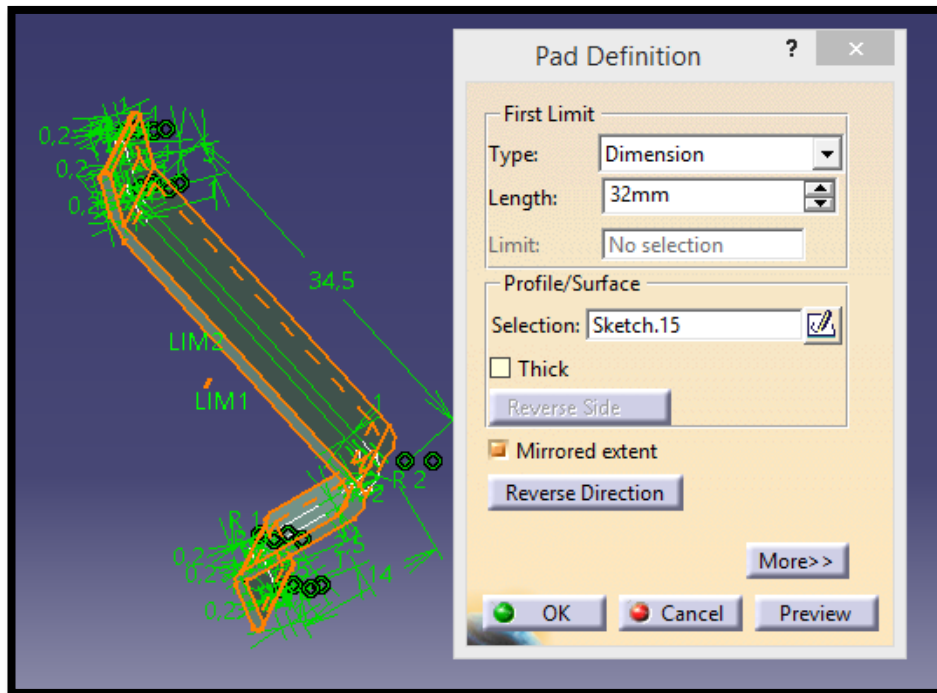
Seat mounting frame 11: Pad sujeción inferior 2
